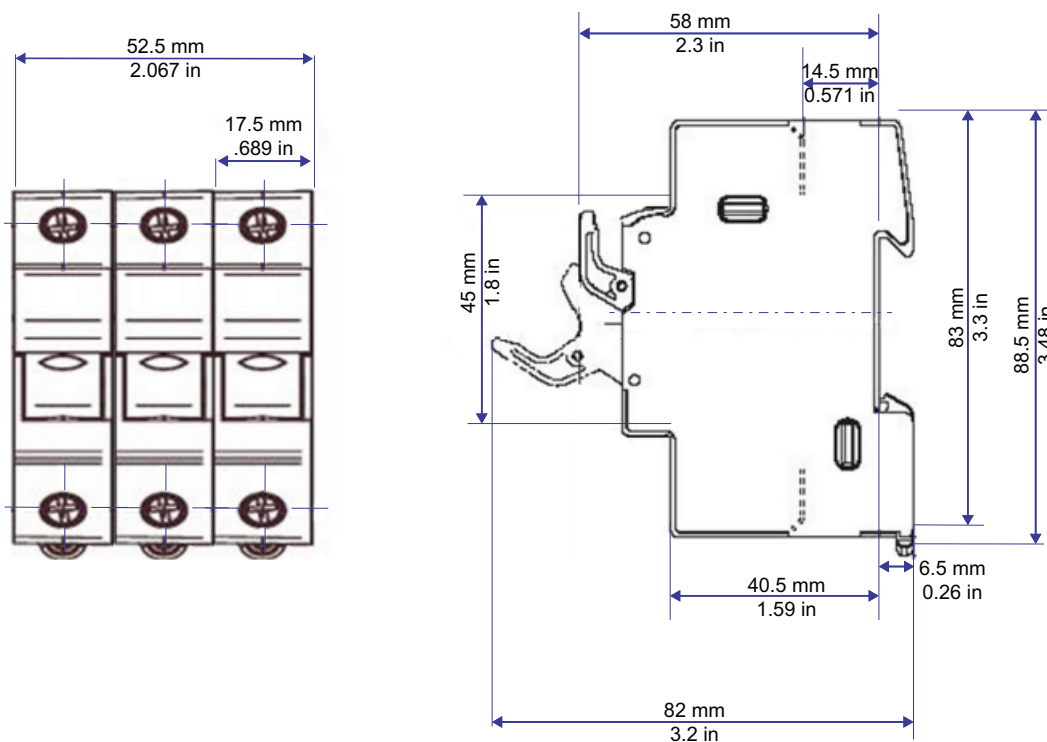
Dimensioni dei portafusibili: US103 (10x38 mm)
